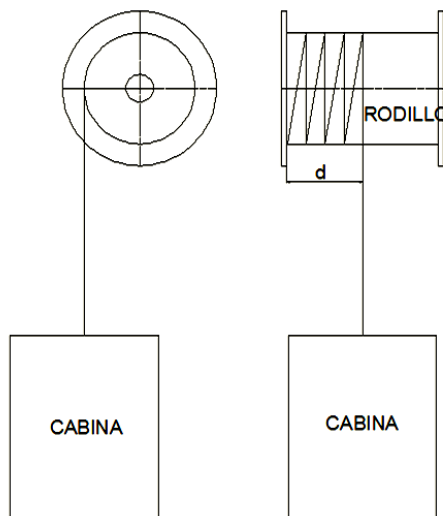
Esquema de sistema de elevación con rodillo enrollado de cable.
